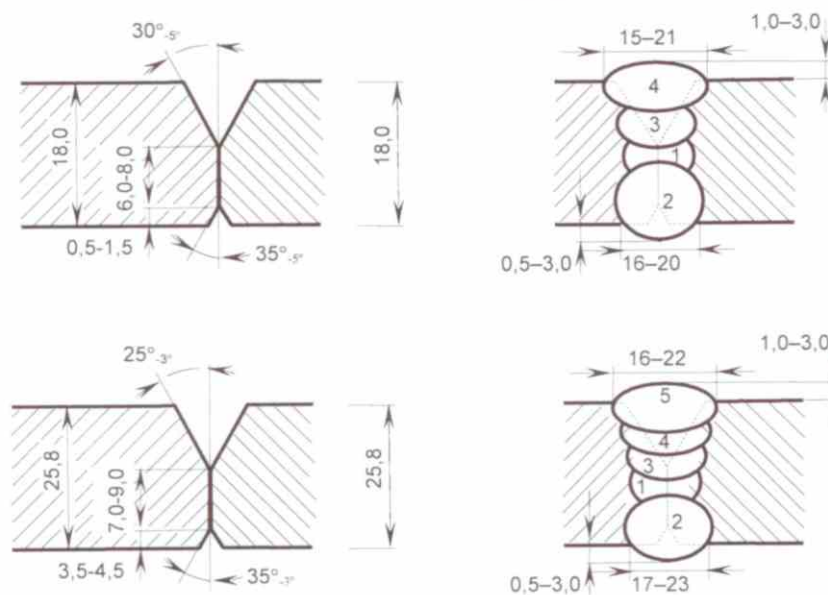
Геометрические параметры сборки и эскиз сварных швов КСС $\varnothing 1220 \times 18,0$ мм класса прочности К52 и $\varnothing 1420 \times 25,8$ мм класса прочности К60, сваренных по технологии автоматической двухсторонней сварки проволокой сплошного сечения под флюсом
